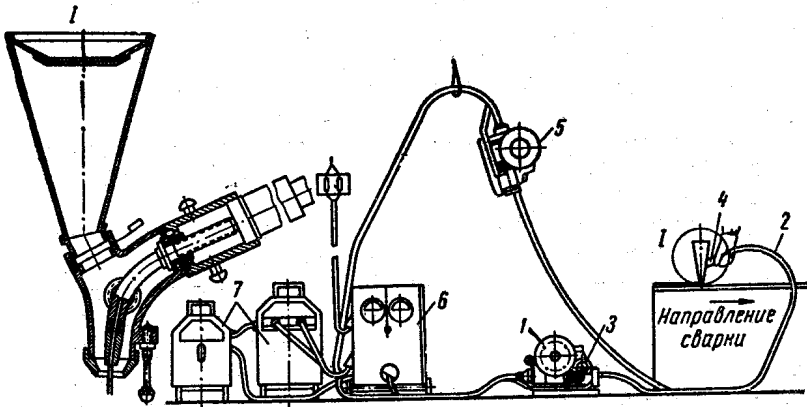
Полуавтомат для сварки под флюсом:
